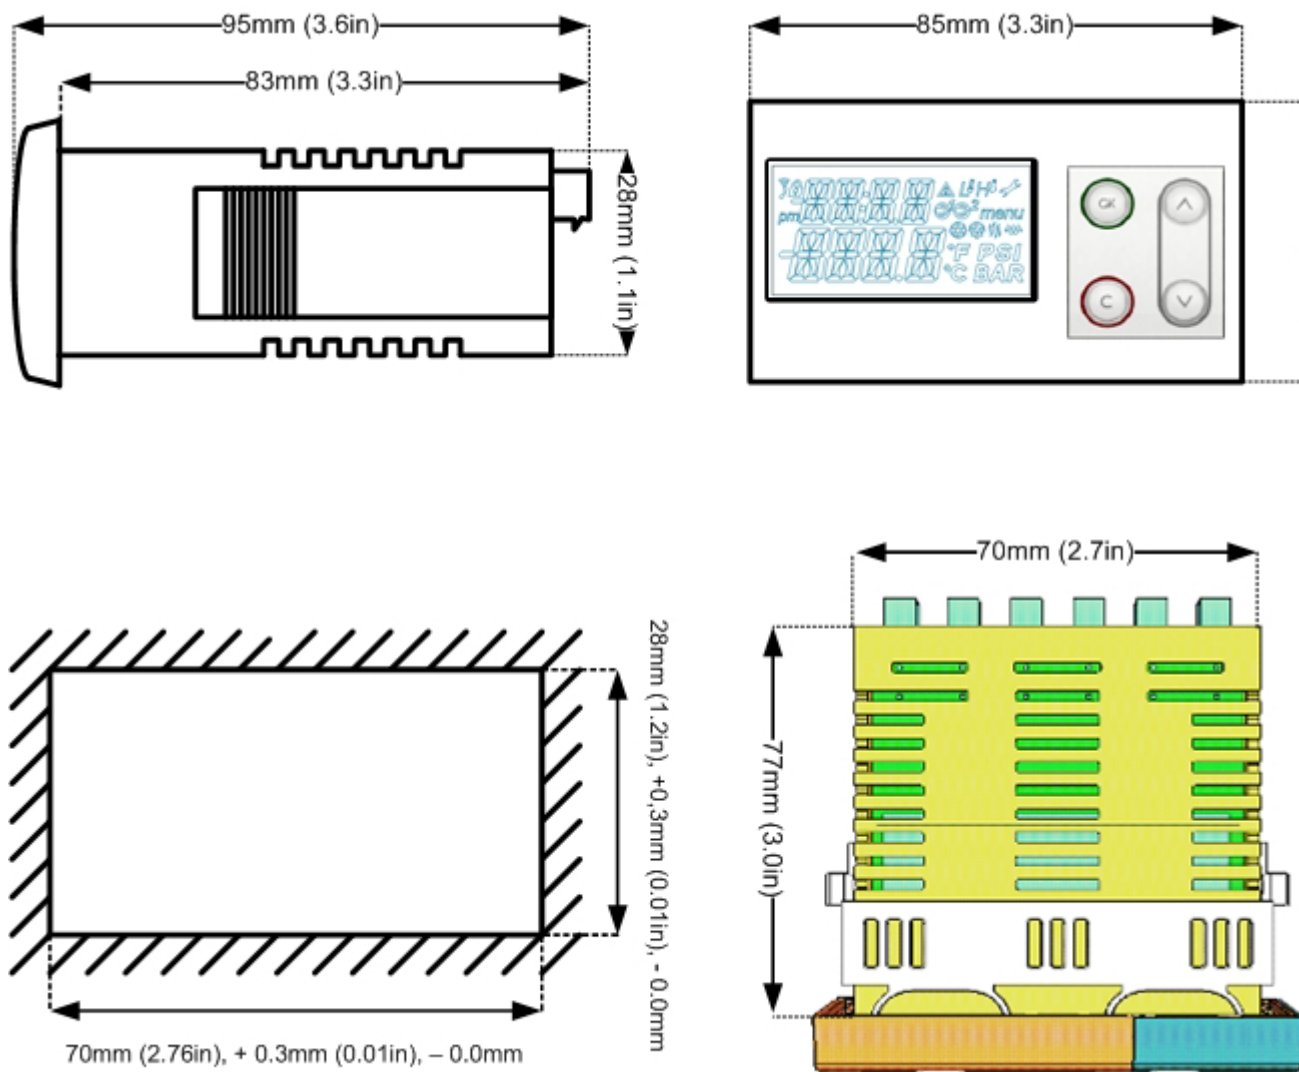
Dimensions du FX06 et de la découpe d'encastrement
